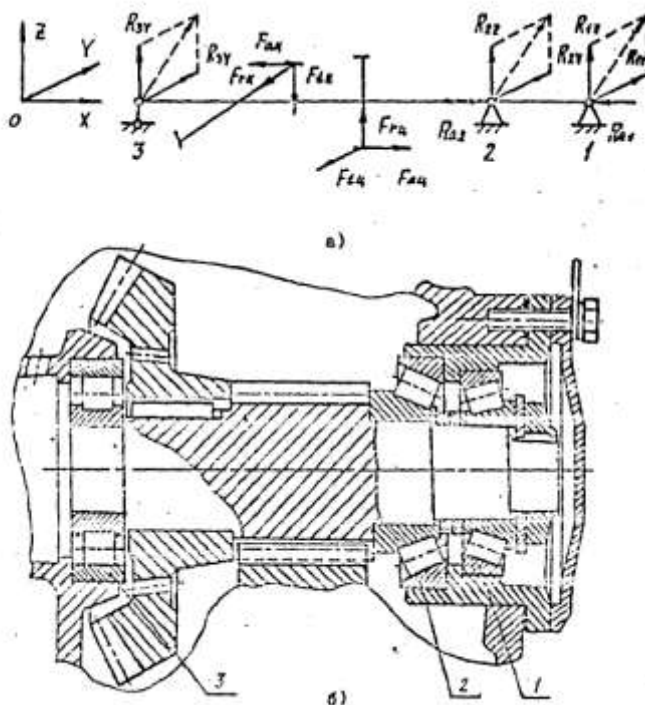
Схема нагружения системой пространственных сил (а) и конструкция (б) вала ведущей цилиндрической шестерни главной передачи автомобиля КамАЗ: 1 - подшипник 27310, 2 - подшипник 27911, 3 – подшипник 102409.
